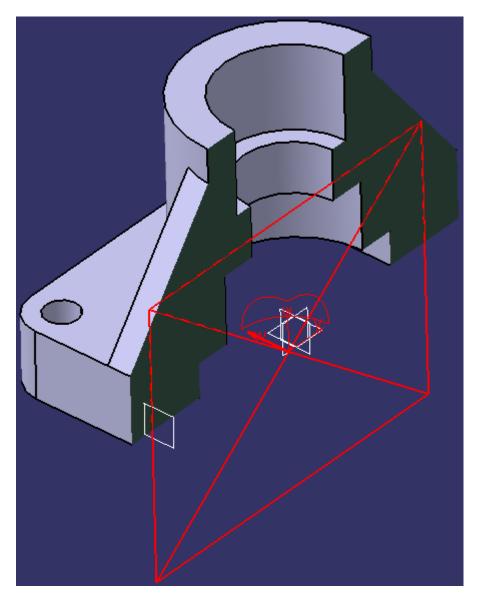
Трехмерная модель детали, изометрический вид с разрезом
